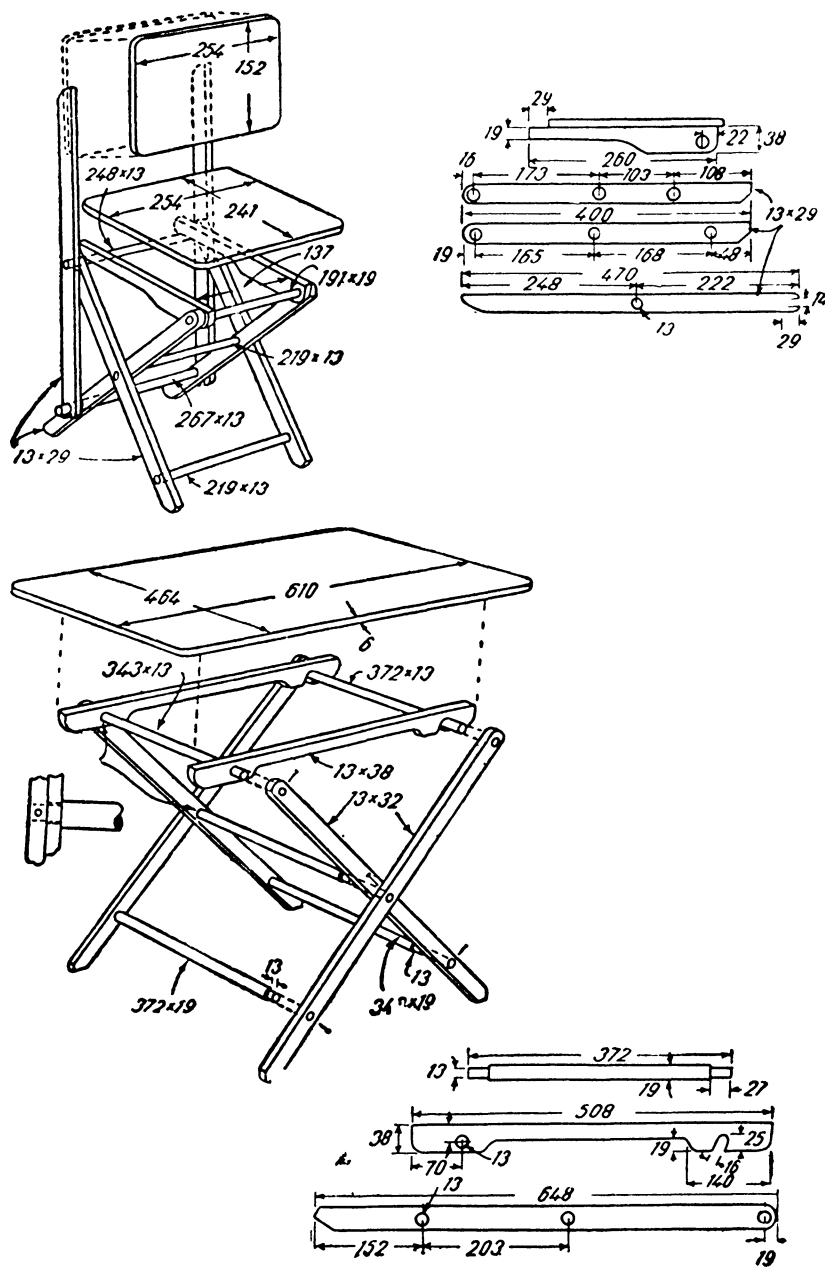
Детали сидения, ножек, брусков спинки и эскизы сборки деталей стула и стола.
